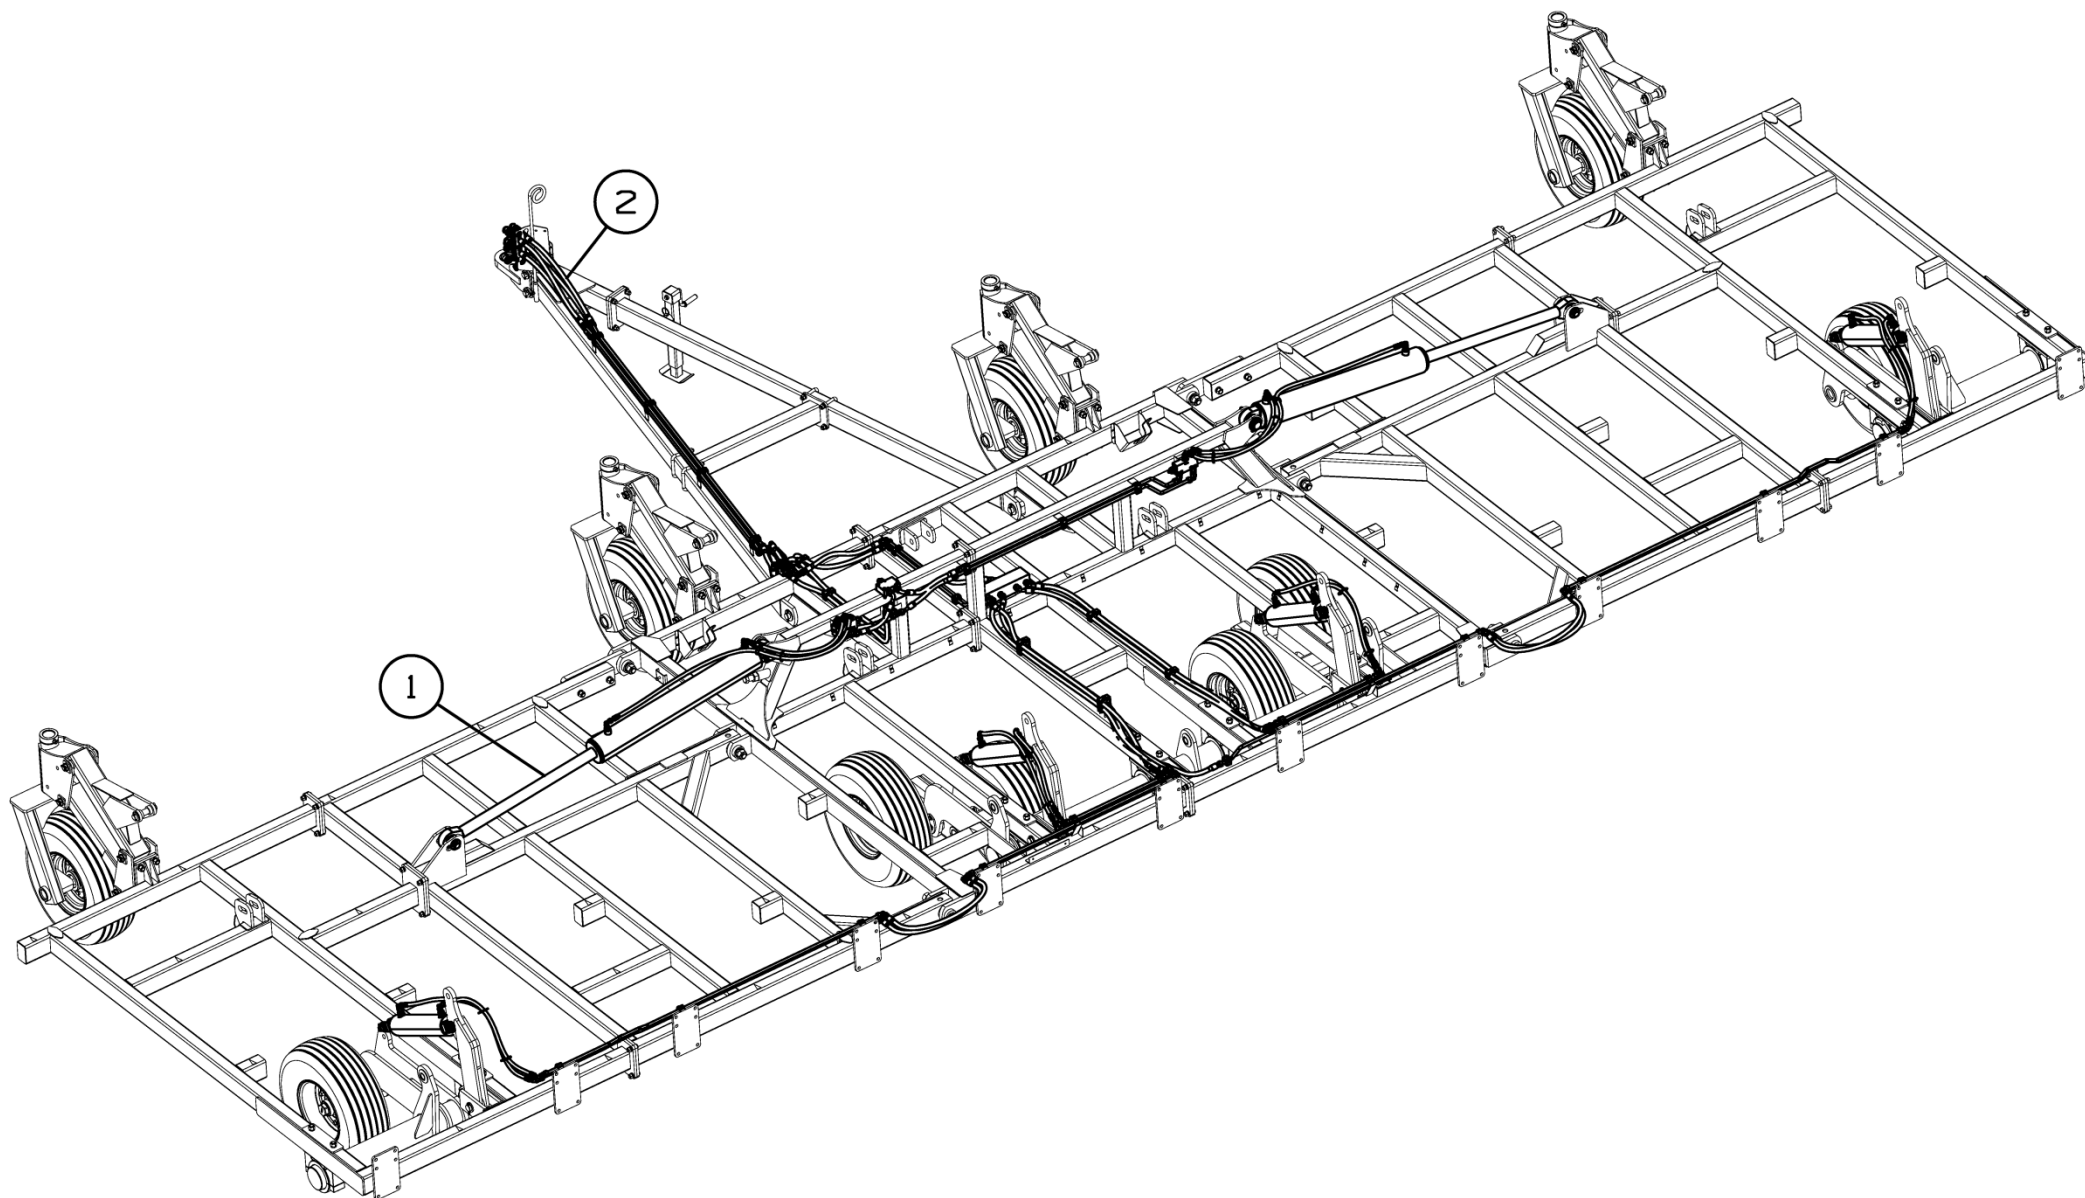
Установка гидрооборудования К-122.12.000В
